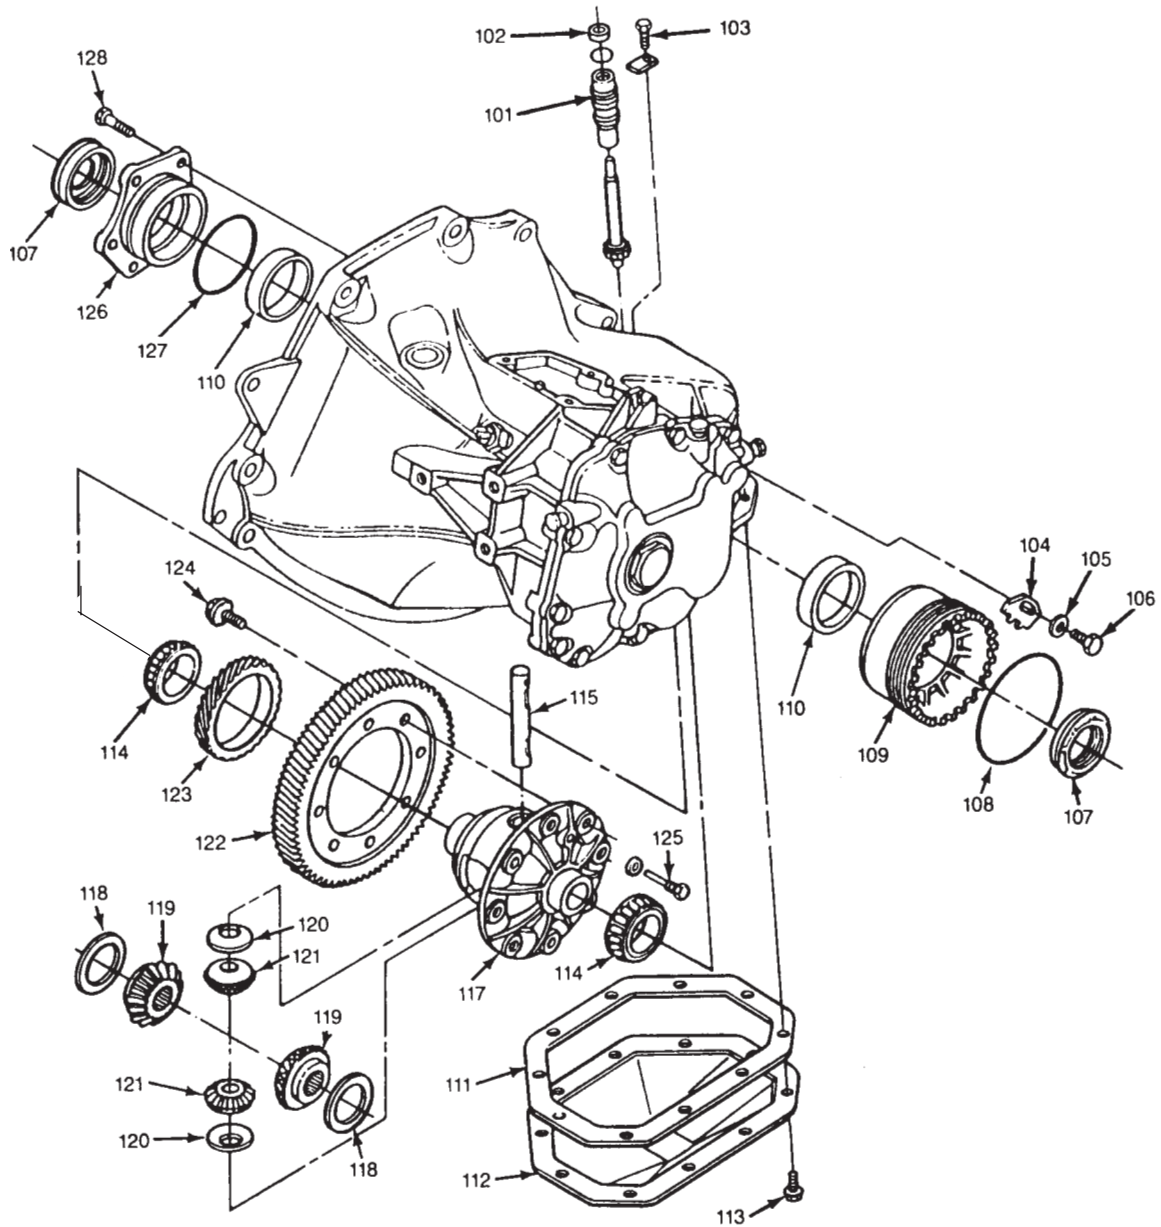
Vedere explodată – pinioane și carcasă F16 (cinci viteze)
